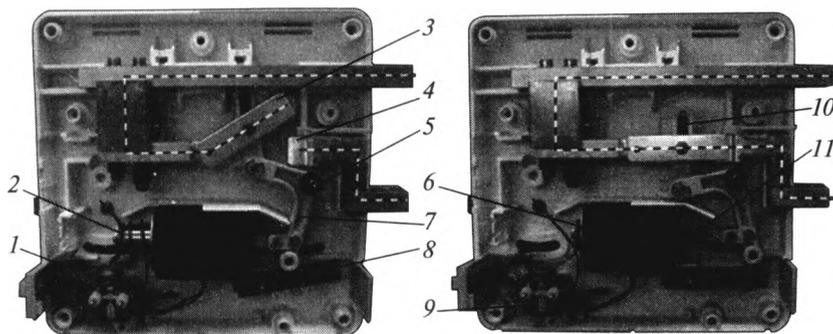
Устройство разъединителя XMS 40.08 010 110 20А:
